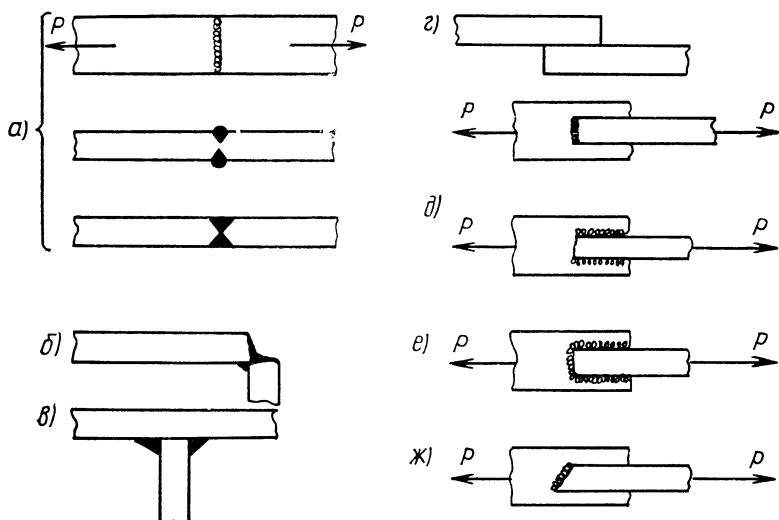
Классификация сварных швов и соединения внахлестку:
